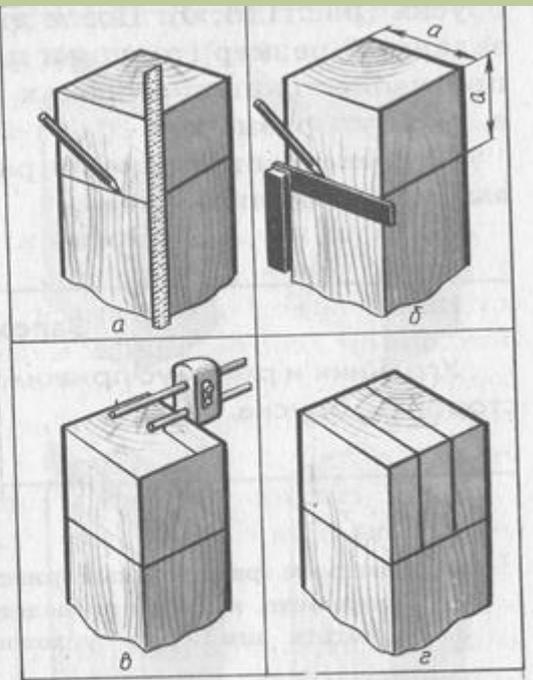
Разметка шипа: а — откладывание длины шипа по линейке; б — нанесение линии разметки по угольнику; в, г — разметка толщины шипа рейсмусом.
